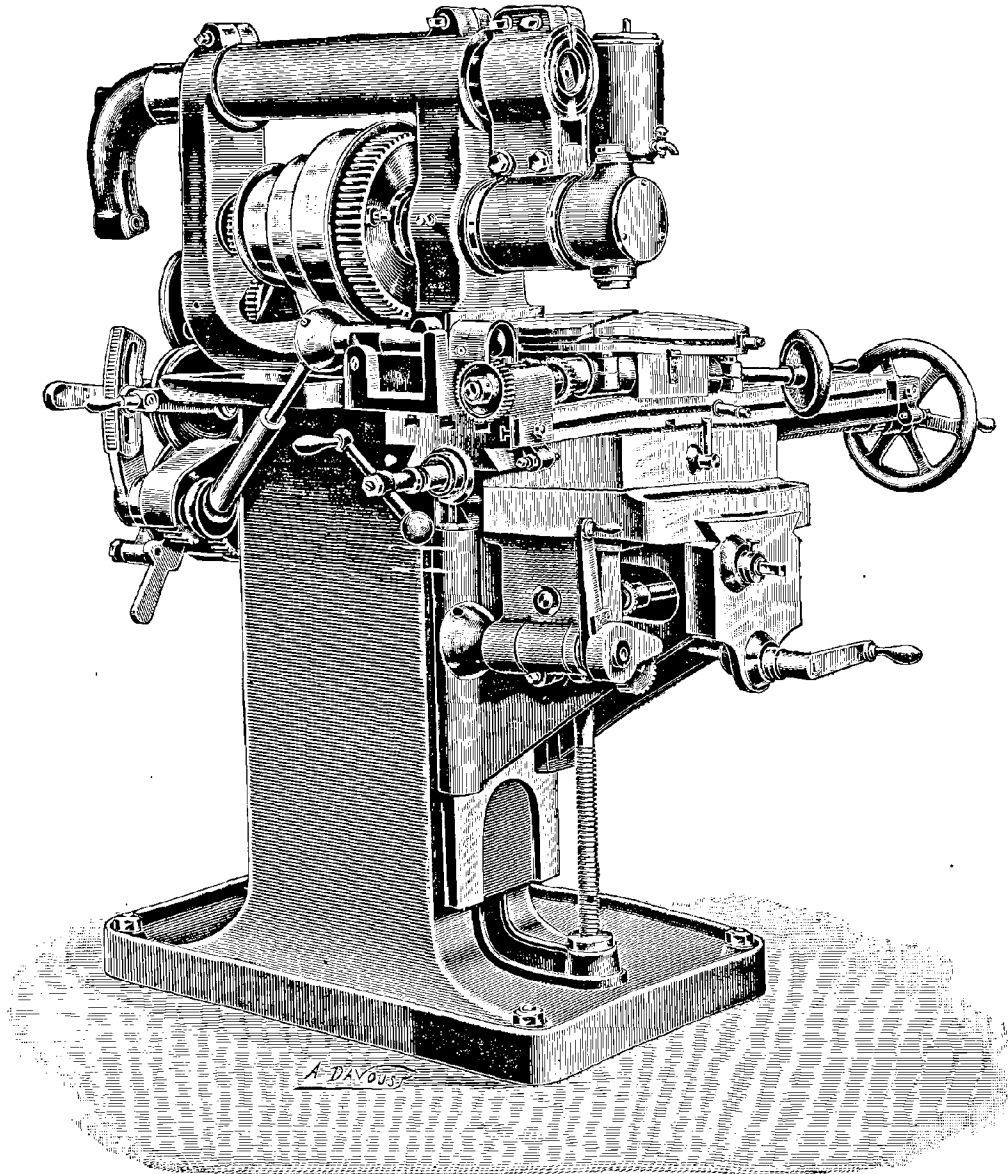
Machine à fraiser de Kemp Smith disposée pour fraiser verticalement.
